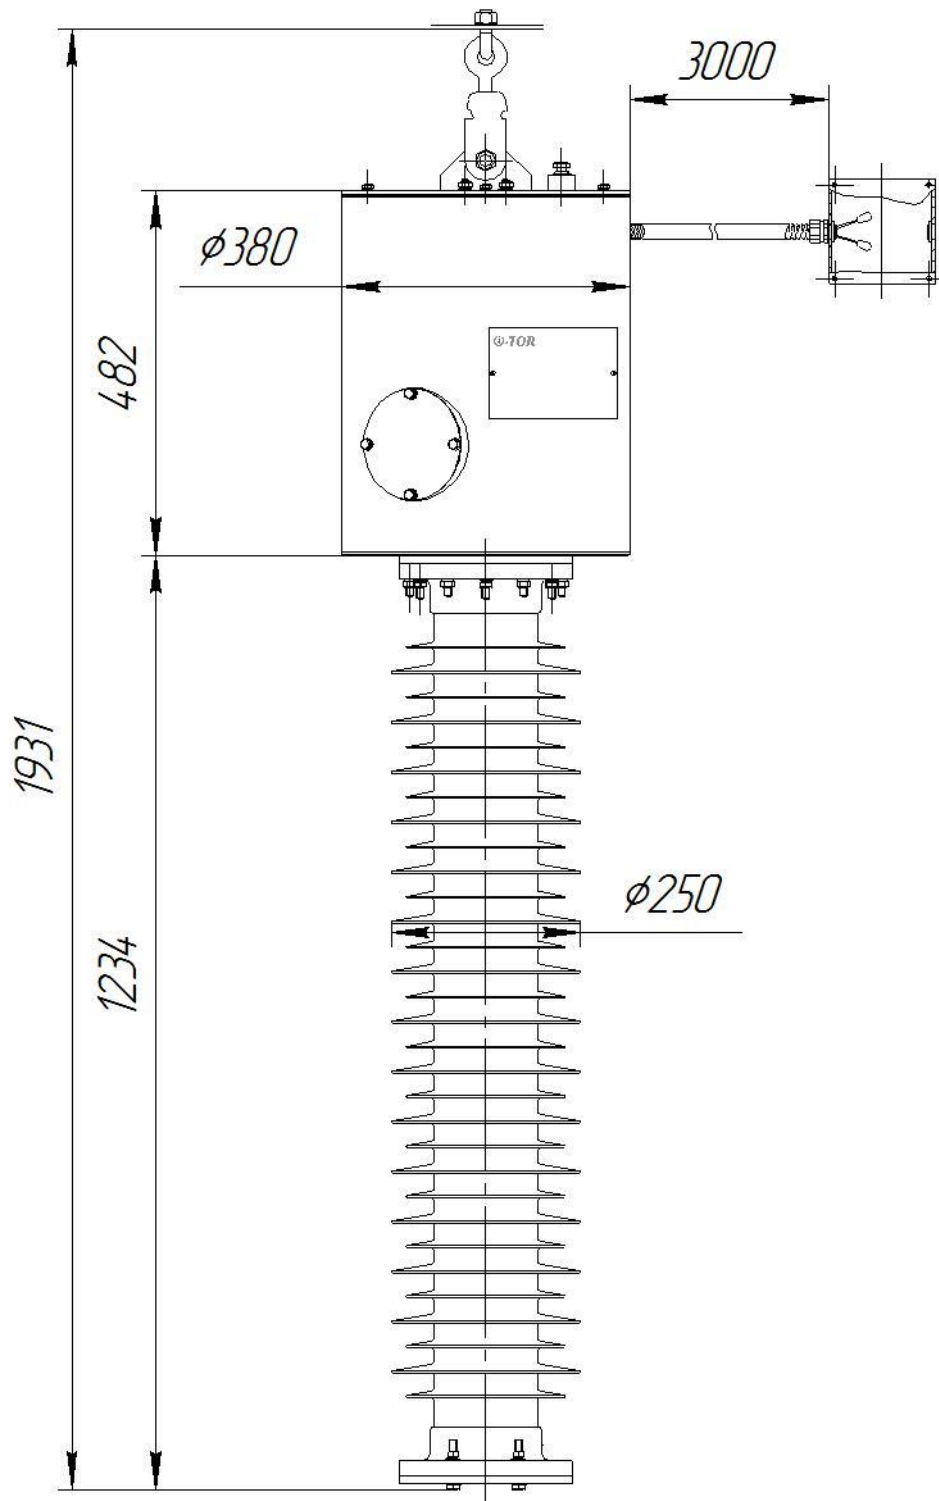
Общий вид и габаритные размеры подвесного высоковольтного модуля
